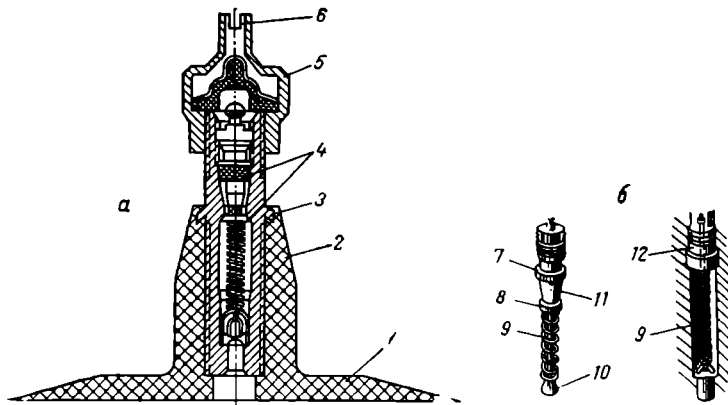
Поперечный разрез металлического вентиля типа ЛК для шин легковых автомобилей (а) и пружинного золотника (б):
